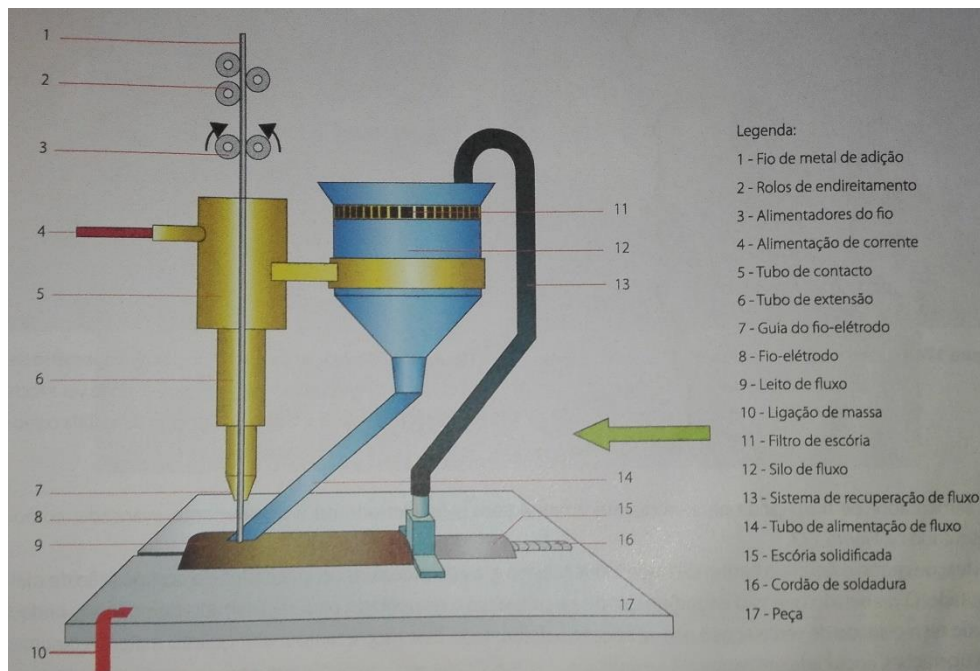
Esquema de soldadura por arco-submerso [17]
